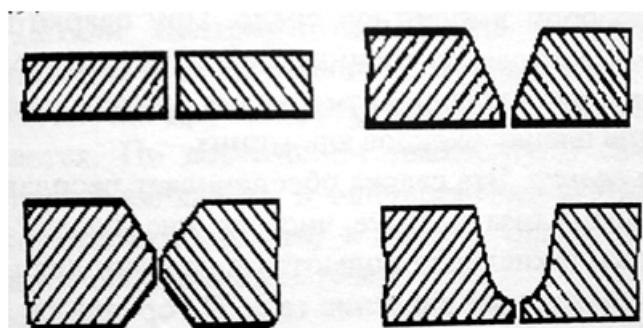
Формы кромок деталей, подготовленных к сварке.
